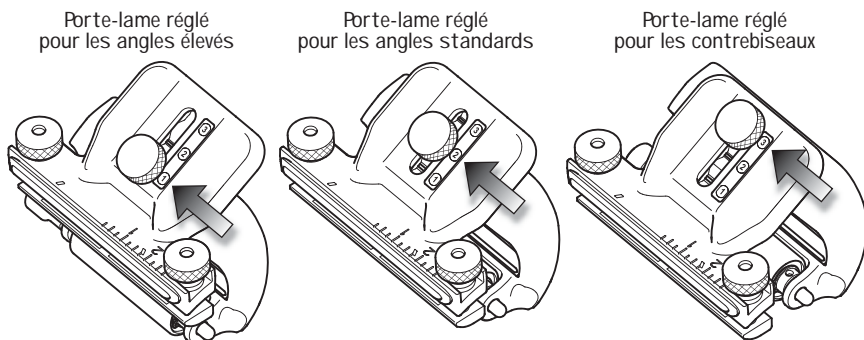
Réglage du porte-lame pour chaque type d'angle de biseau
